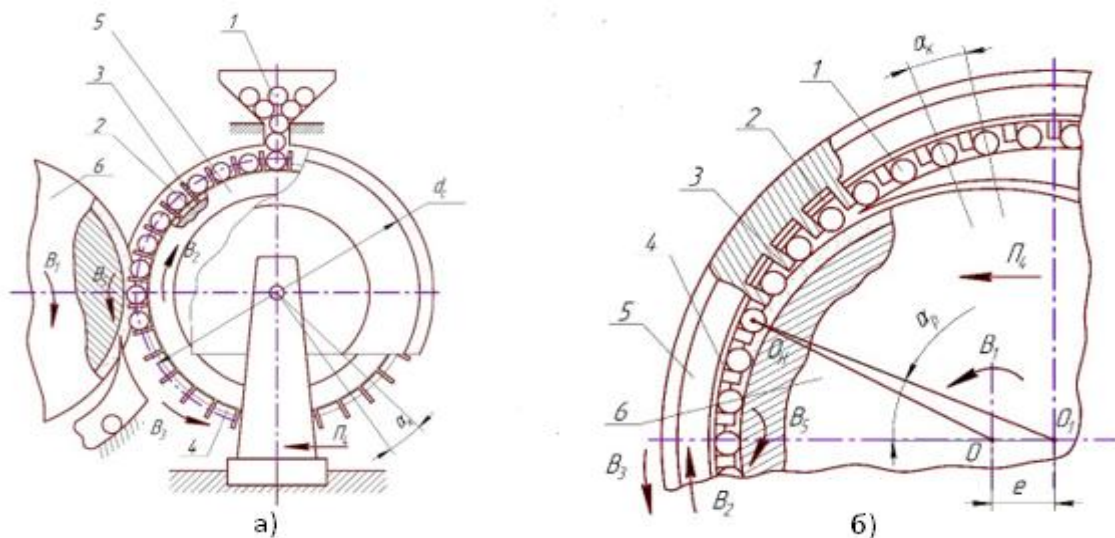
Кінематичні схеми верстатів з робочим клиновим зазором: а) зовнішнім; б) внутрішнім
